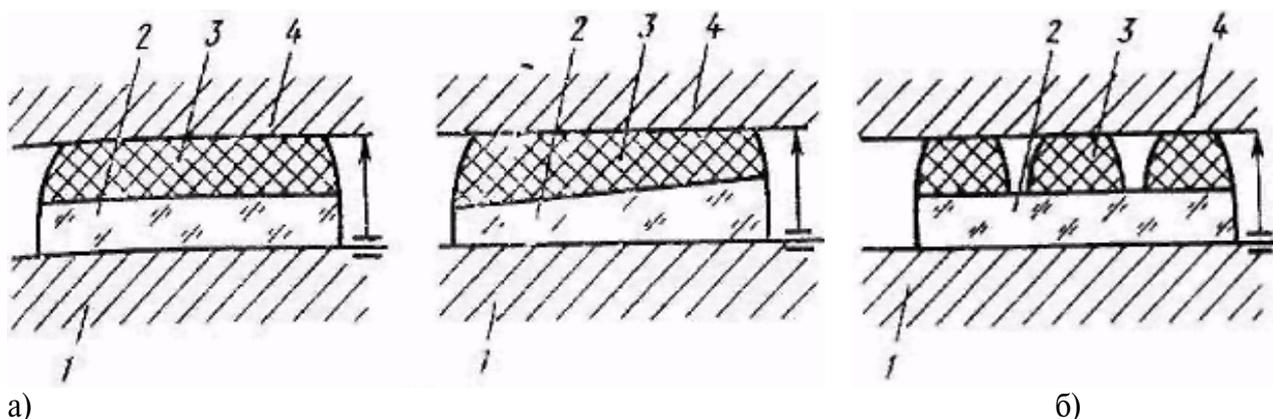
Эластичное крепление заготовок пластин и клиньев:
